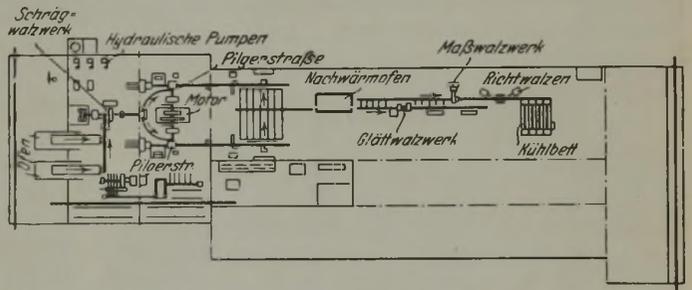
Pittsburgh Steel Products Co., Werk Allenport, Pilgerstraße.
